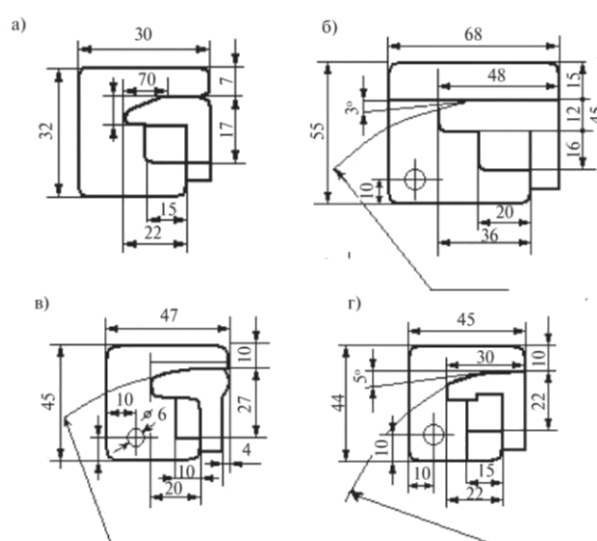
Шаблоны для проверки профиля и износа контактов контактора:
